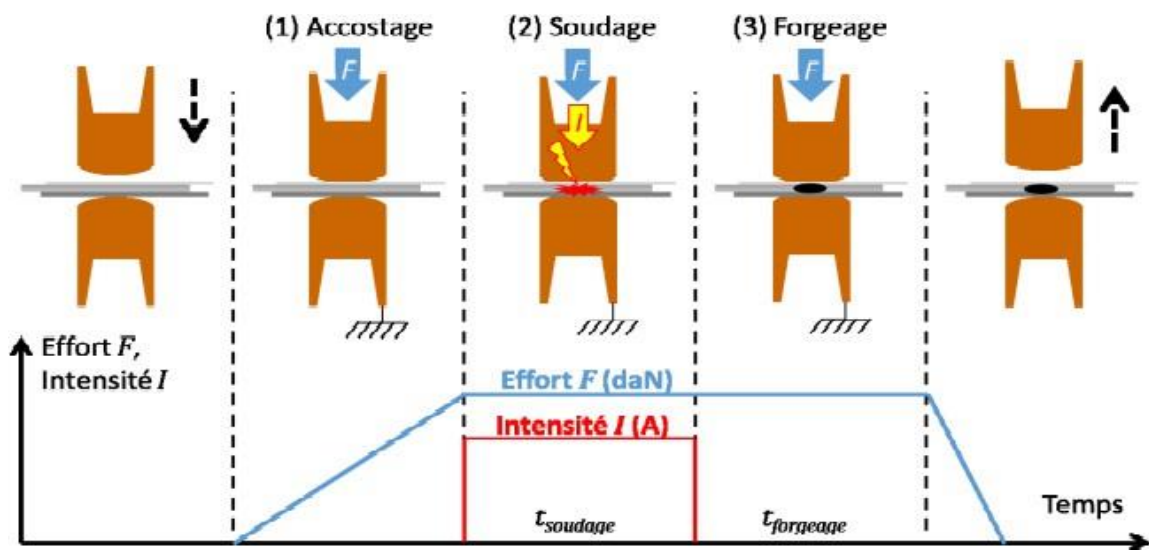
Schéma de principe du soudage par points [4]
